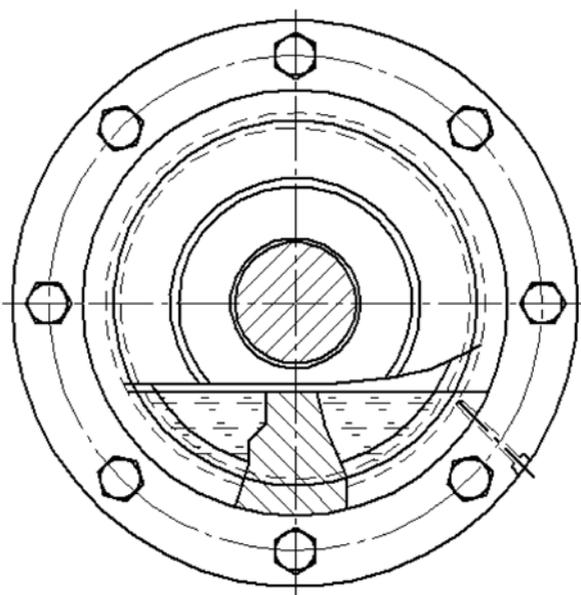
Схема проверки уровня масла в зубчатой муфте
